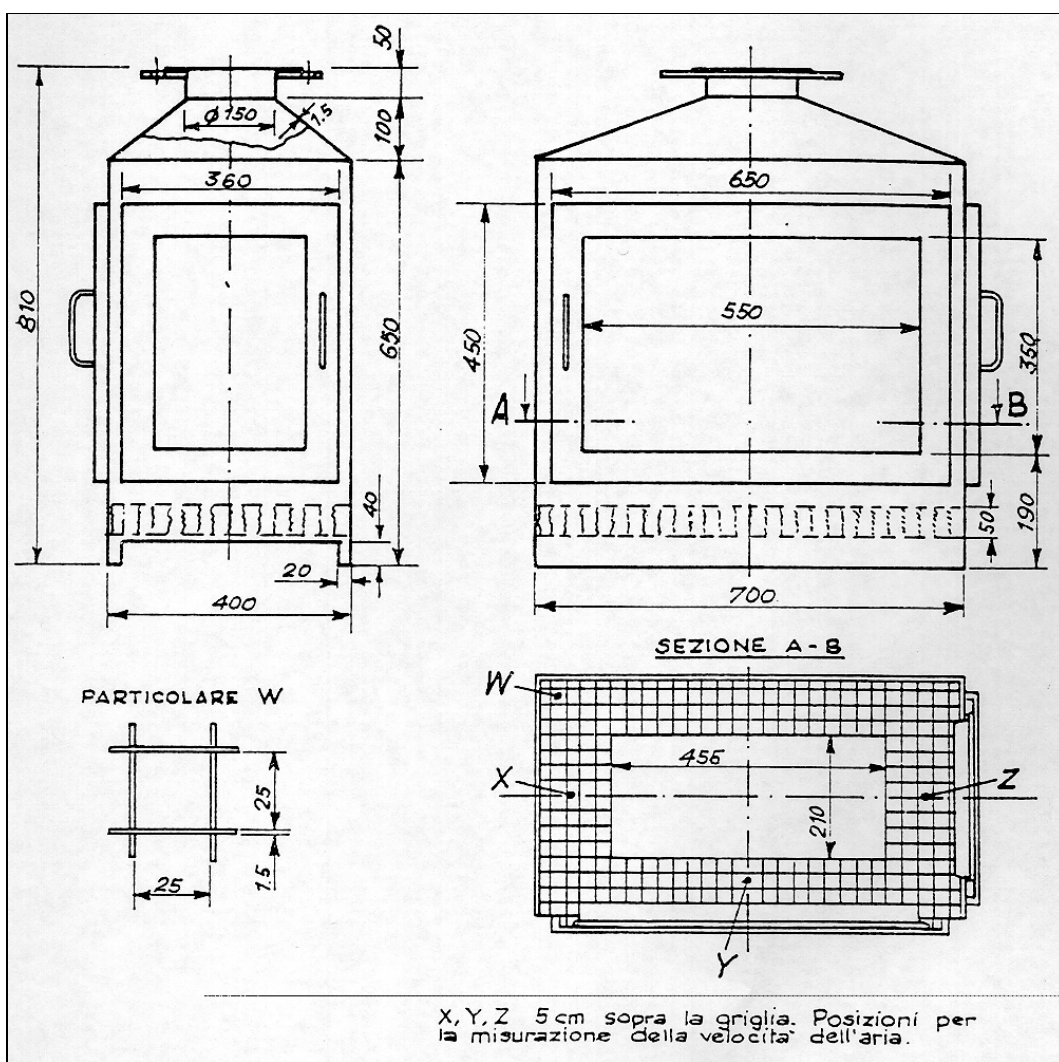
CAMERA DI COMBUSTIONE PER IL METODO DI PROVA CSE RF 2/75 A
